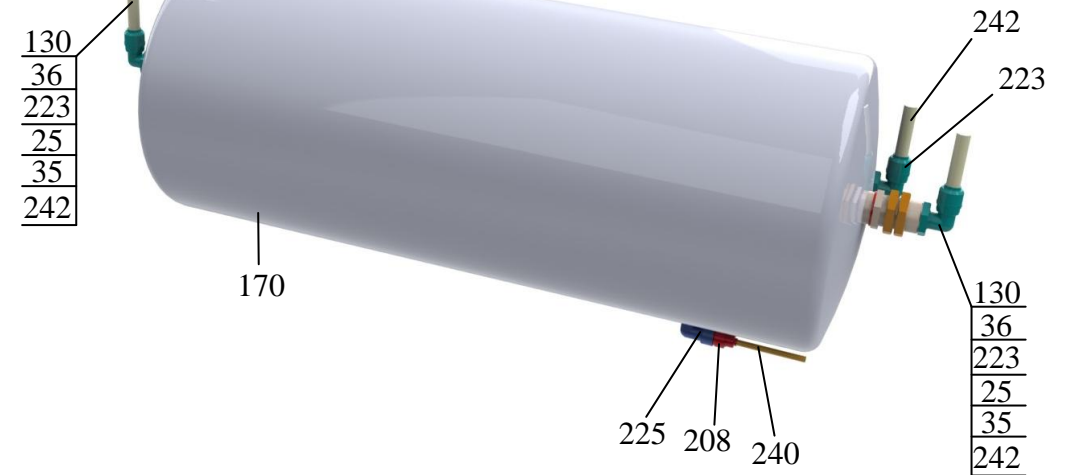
(лист 1 из 2) – Установка ресиверов
